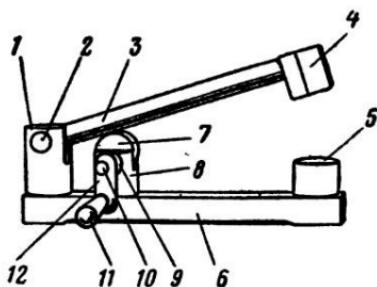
Модель рычажного молота: 1 — кронштейн рычага; 2 — ось рычага; 3 — рычаг; 4 — боек; 5 — «наковальня»; 6 — основание; 7 — ведущий диск; 8 — стойка; 9 — упорное кольцо; 10 — вал привода; 11 — ручка; 12 — рычаг ручки.
